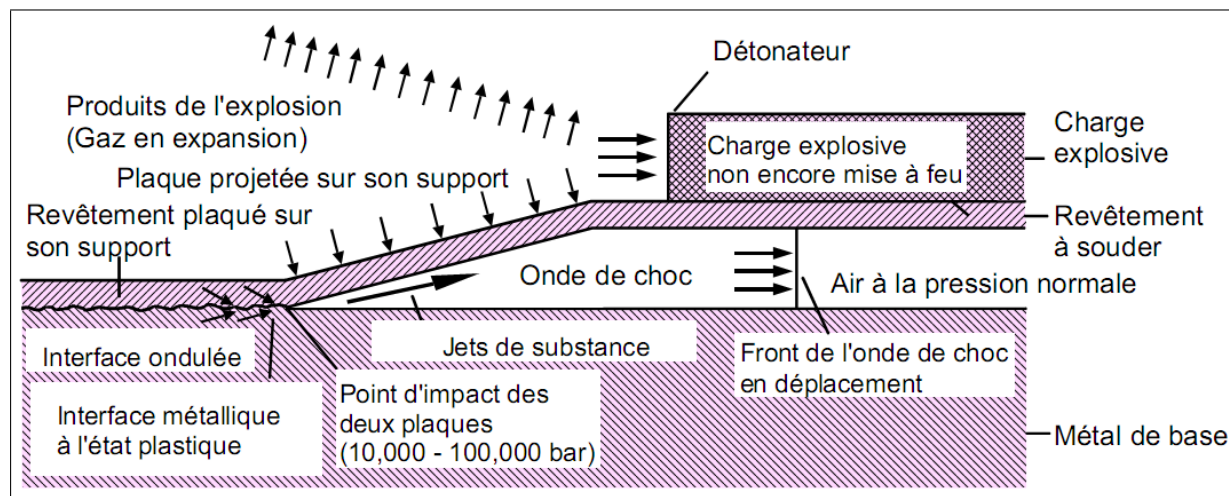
Schéma de principe du soudage par explosion [45].
